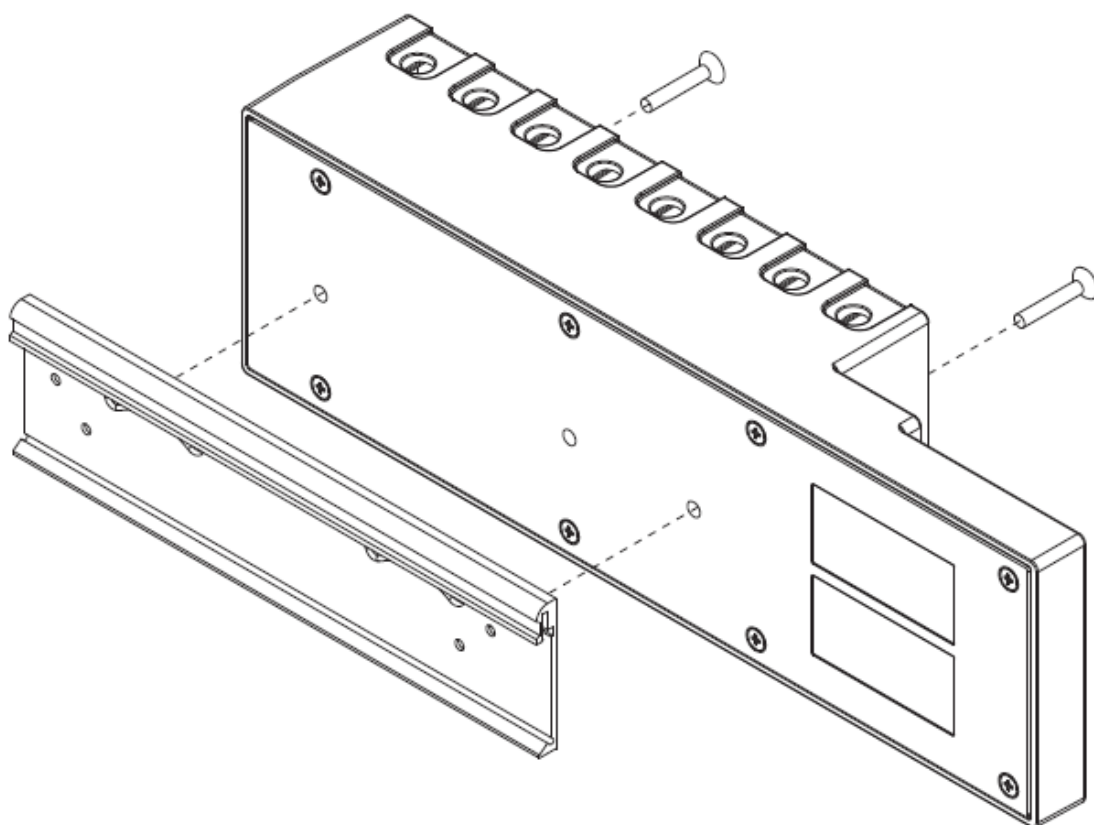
Установка клипсы крепления DIN на cRIO-9068.
